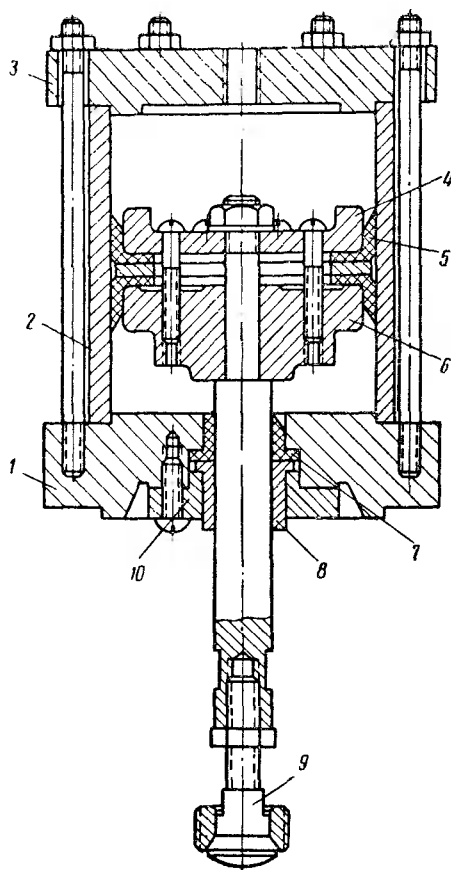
Пневмозажим универсального стенда для сборки головок цилиндров:
